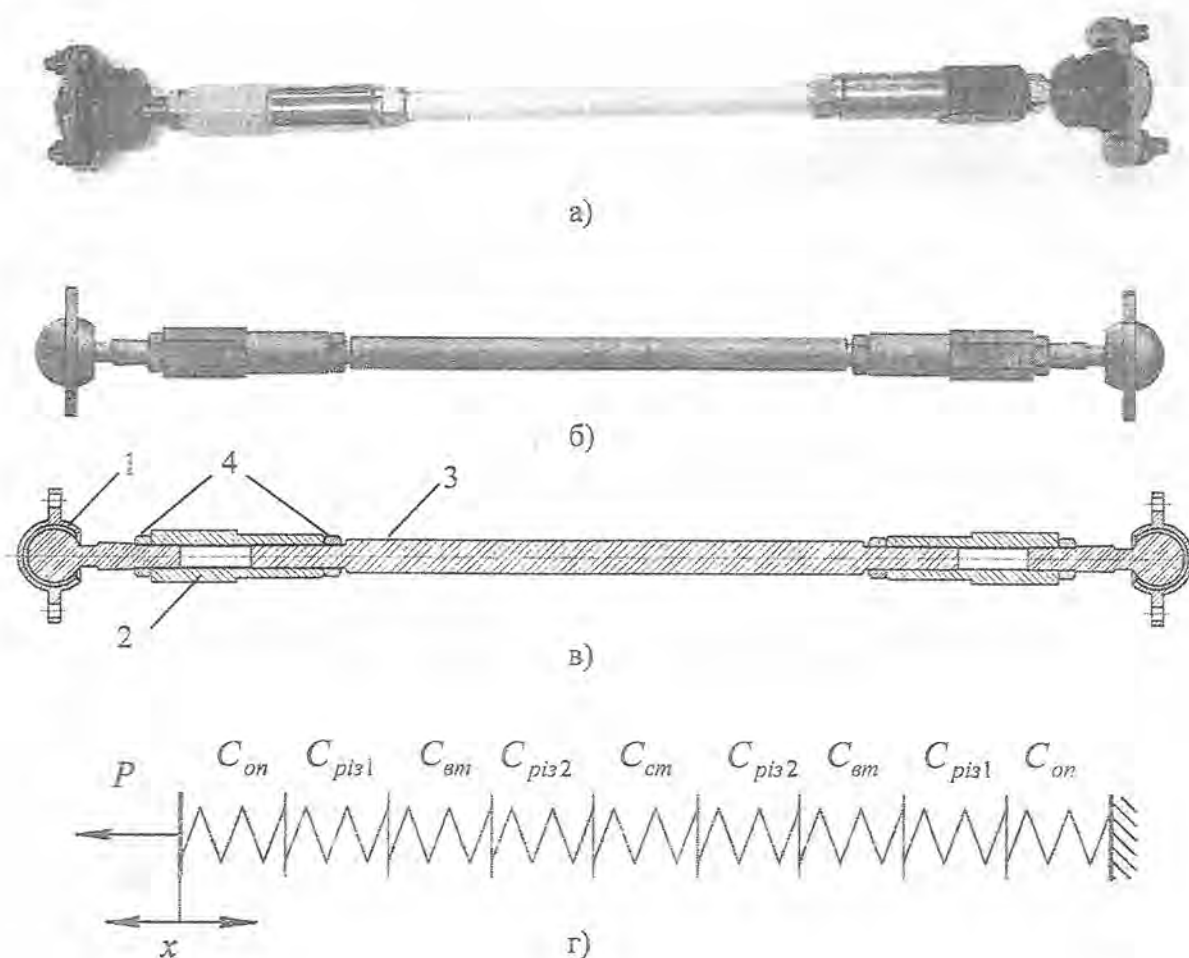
Штанга постійної довжини: а) – виготовлений зразок; б) і в) – 3D і 2D CAD модель конструкції штанги, відповідно; г) – розрахункова схема. 1 – шарова опора; 2 – втулка; 3 – стержень; 4 – контргайка
